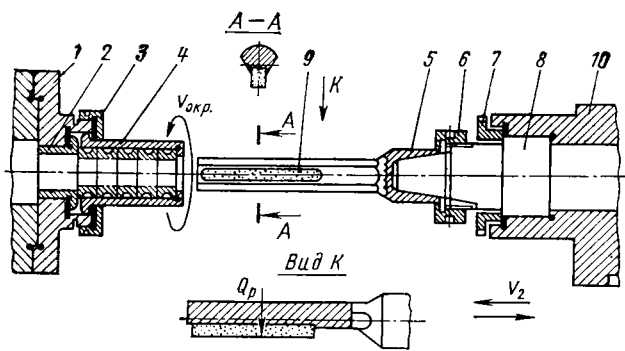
Принципиальная схема абразивной расточки: 1 — планшайба; 2 — опорная втулка; 3 — зажимная втулка; 4 — обрабатываемые кольца; 5 — оправка крепления абразивных брусков; 6 — гайка; 7 — фланец; 8 — корпус механизма подачи; 9 — абразивный брусок; 10 — корпус бабки шлифовального шпинделя
